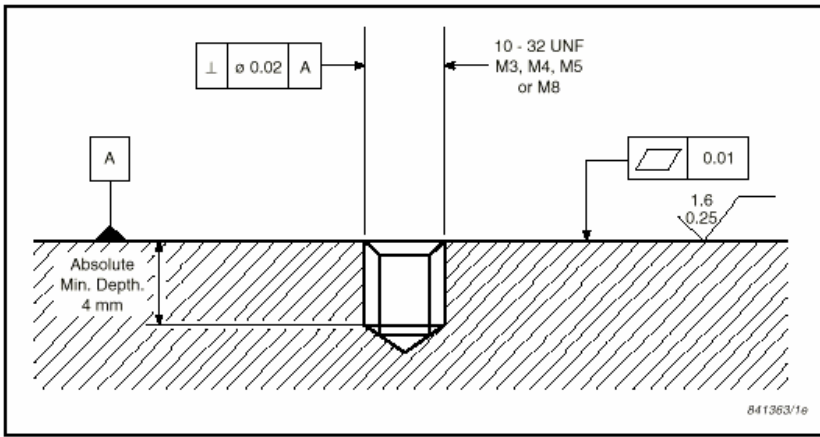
Рекомендованные допуски для установочных поверхностей. Размеры и символы согласно ISO 1101
